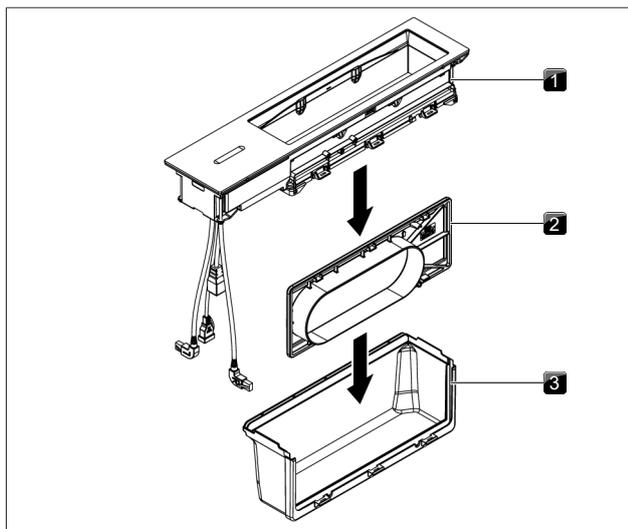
Ensamblaje de los componentes individuales del extractor de superficie
